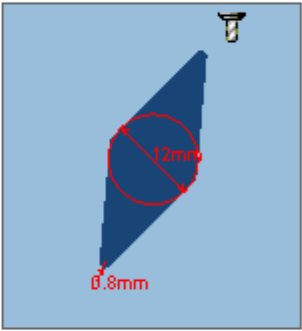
Пластинка різця «CP-B1208D-M5W 4425»
